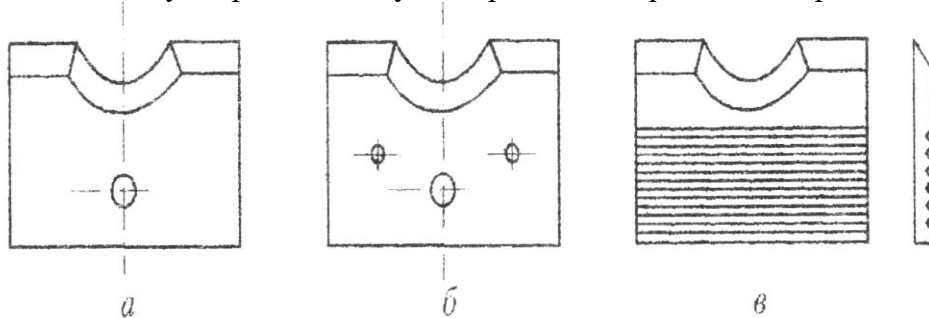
Конструкції профільних ножів: *a* - з отвором для головки регульовального гвинта; *б* - те ж і установочними отворами; *в* - з рифленнями на опорній поверхні.
